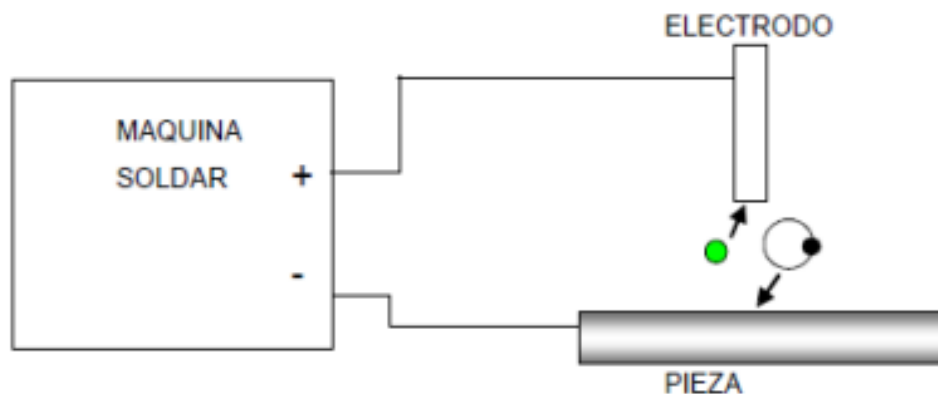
Esquema de Polaridad Inversa de la Soldadora GMAW.
